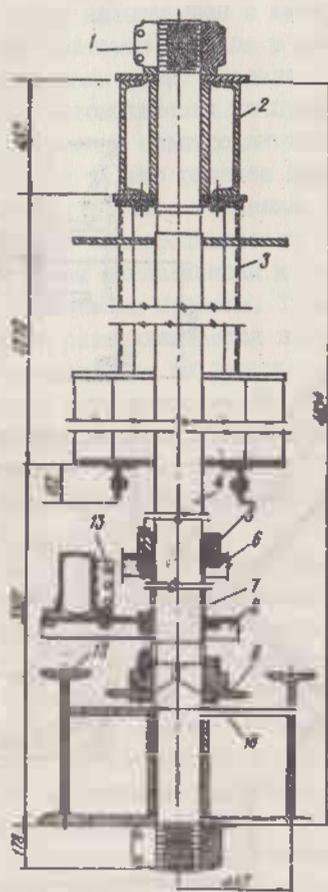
Схема установки колонны и сопряженных с ней деталей пресса фирмы "Континенталь/Мосс-Гордип": 1 - гайка разъемная; 2 - верхняя траверса; 3 - стойка под верхнюю траверсу; 4 - колонна; 5 - крестовина для крепления ящиков; 6 - труба; 7 - обечайка; 8 - кривошип фиксаторов; 9 - звездочка привода поворотов ящиков; 10 - опора подшипника; 11 - подшипник; 12 - нижняя траверса; 13 - механизм фиксатора
